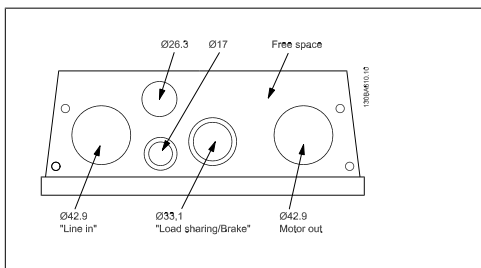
Orificios de entrada para cables en el armario B2. La utilización que se sugiere de los
